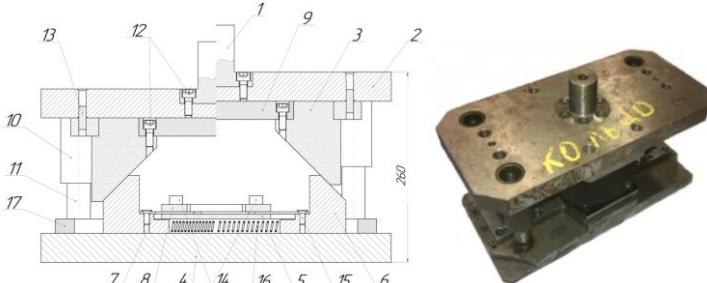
Штамп сжатия для изготовления кольцевых деталей: 1 – цилиндрический хвостовик; 2 – плита верхняя; 3 – упоры; 4 – плита нижняя; 5 – плита опорная; 6 – подвижные упоры; 7 – элементы сжатия (пуансоны); 8 – крышка прижимная; 9 – плита установочная; 10 – втулка направляющая; 11 – направляющая нижней плиты; 12 – винты крепления элементов штампа; 13 – штифт; 14 – винты крепления прижимной крышки; 15 – винт крепления пуансона; 16 – пружина возврата; 17 – плита подвижных упоров
